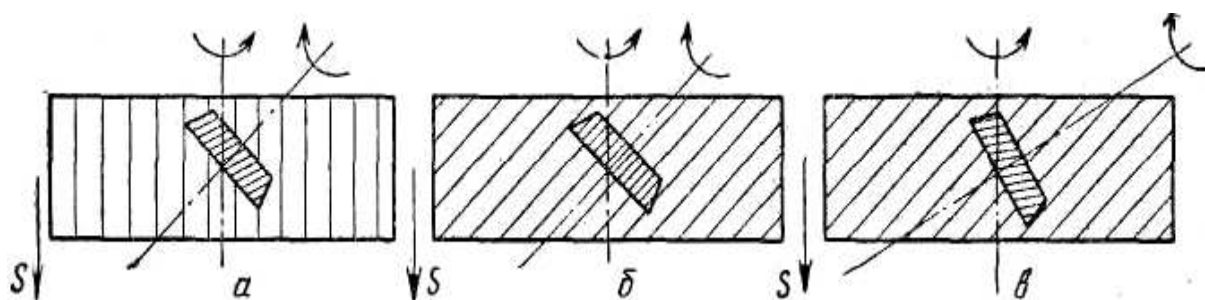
13. Возможные схемы зуботочения цилиндрических колес
